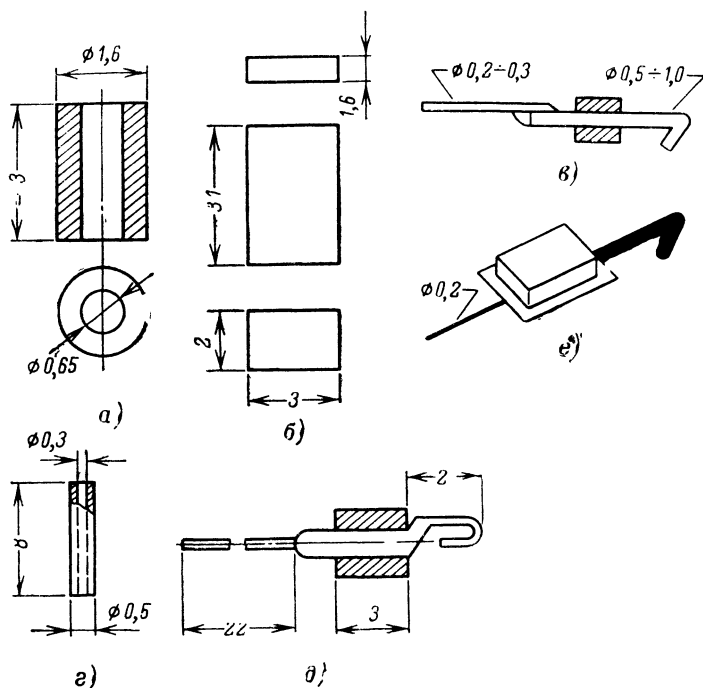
Цилиндрический и прямоугольный роторы датчиков (а и б), крепление (в) цилиндрического ротора с помощью медной трубки (г), медной проволоки (д) и крепление прямоугольного ротора (е).
